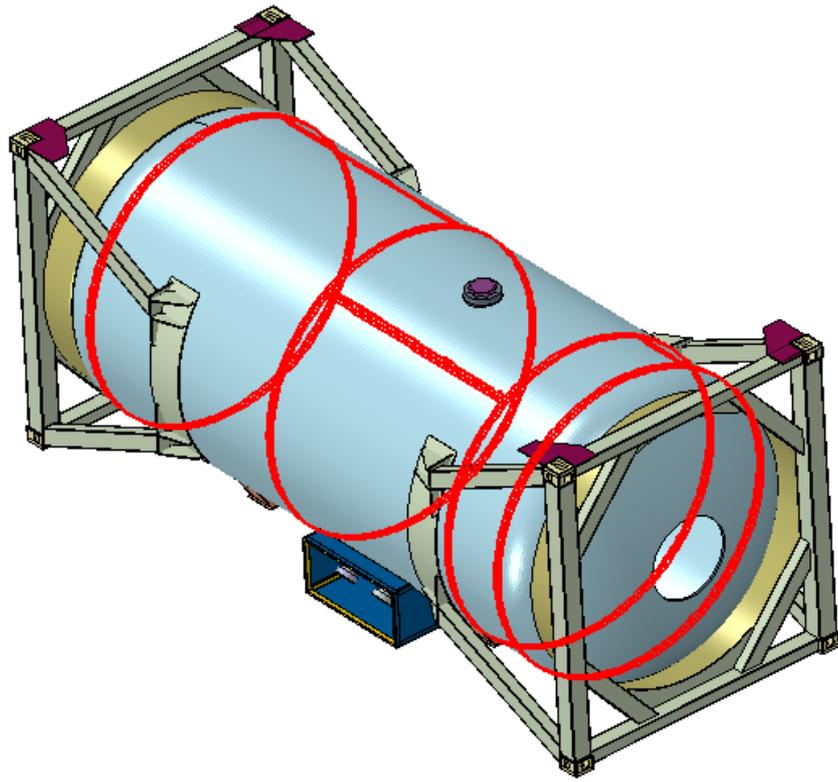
Зоны сварных швов цистерны
